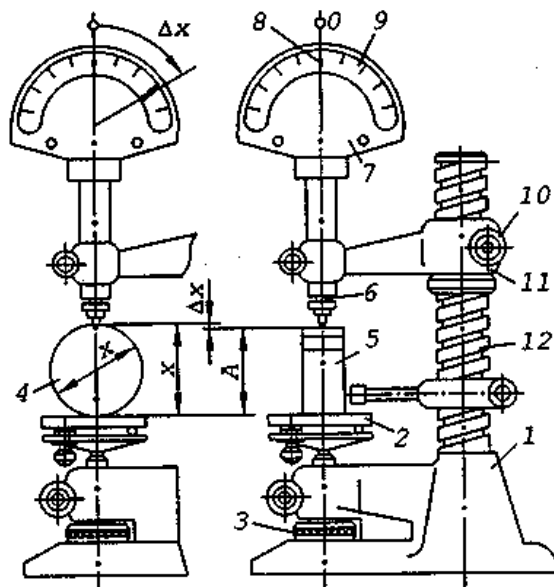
Контрольно-вимірювальний пристрій для дослідження відхилень форми поверхонь
